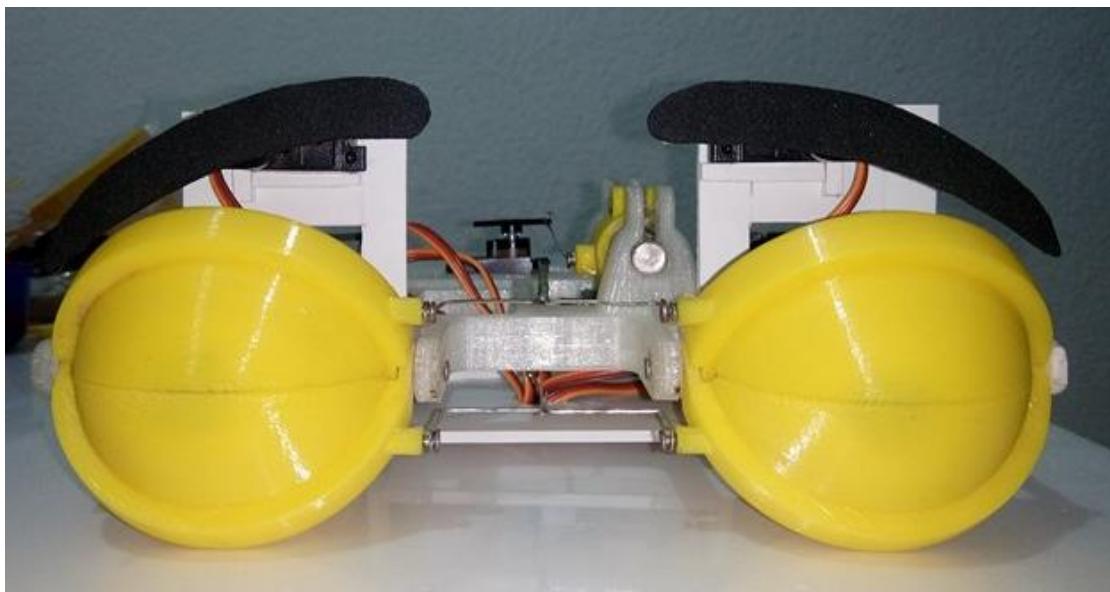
Vista frontal del montaje de las cejas en su correspondiente estructura
